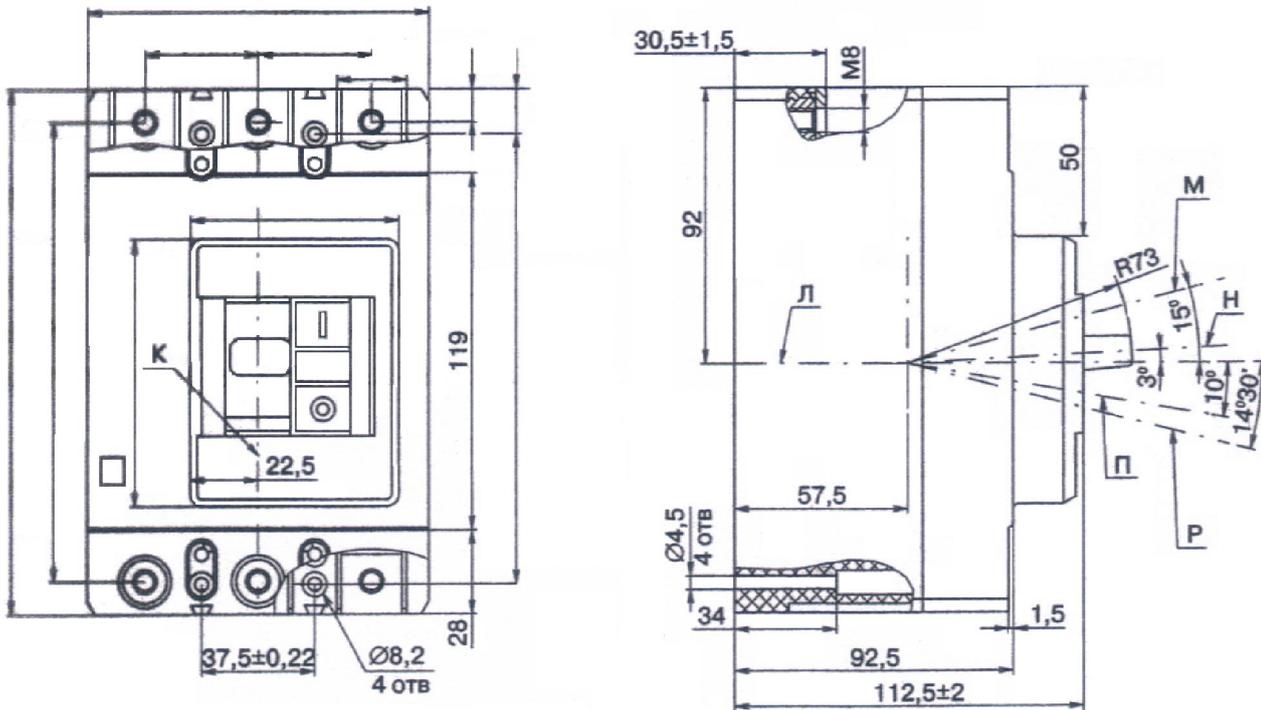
Габаритные размеры выключателя ВА57Ф35
